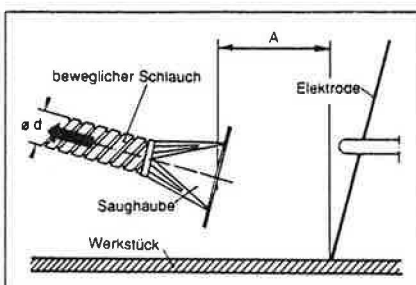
Trichterförmige Absaughaube zum Erfassen der Rauche beim Elektro-Schweißen
